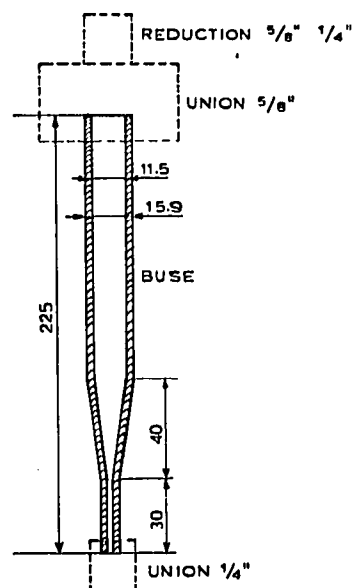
Coupe de la buse de remplissage. Les dimensions sont exprimées en mm.
